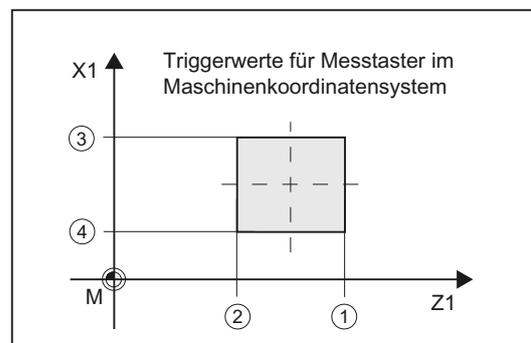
Werkzeugmesstaster, maschinenbezogen (G18)
